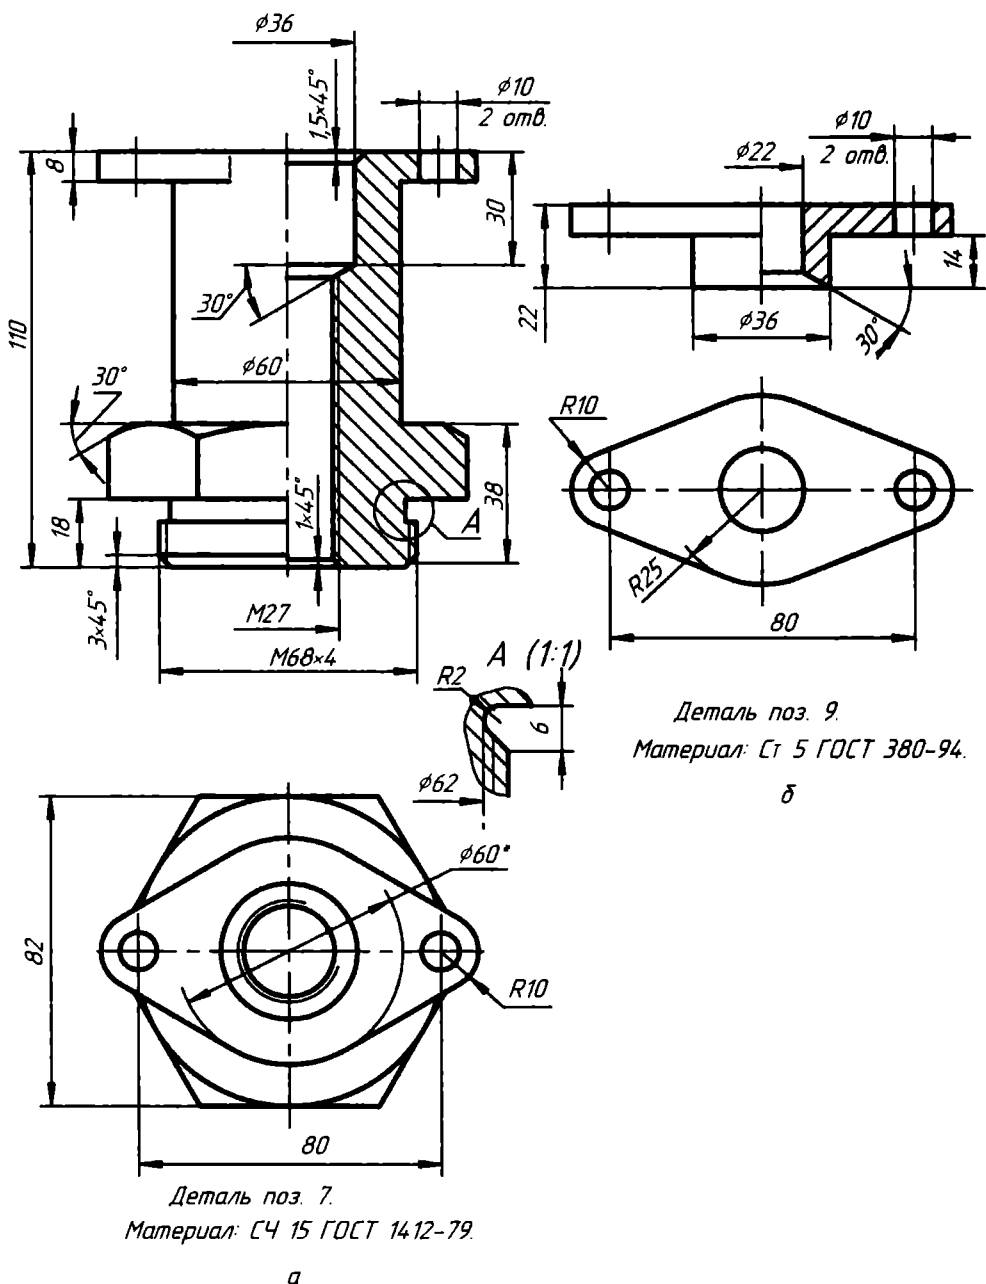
Чертежи: а — крышки; б — фланца вентиля
